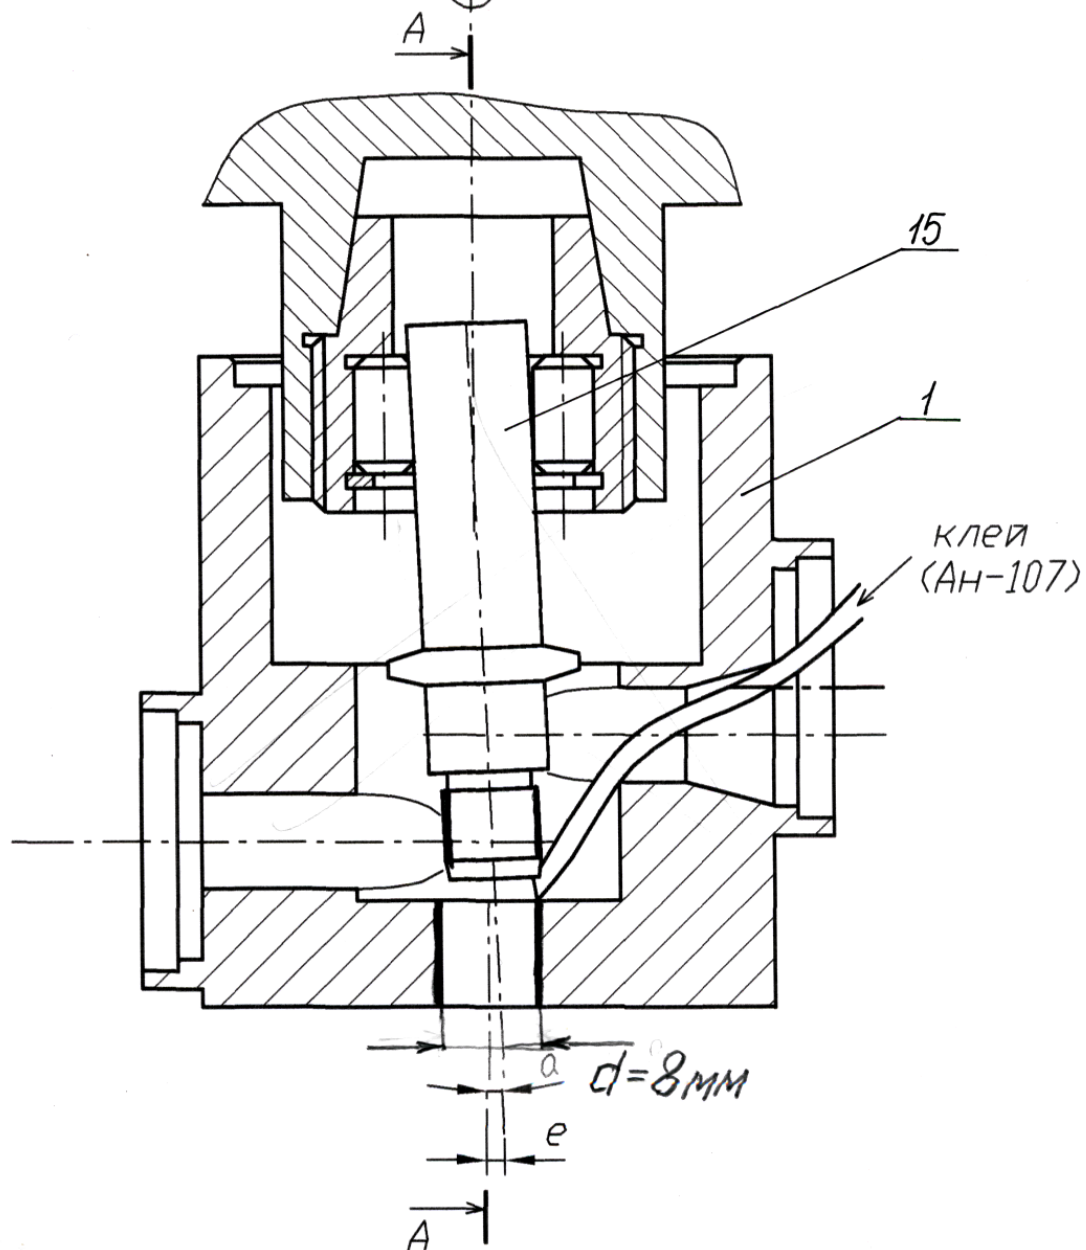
Эскиз установки шпинделя токарного станка в корпус.
